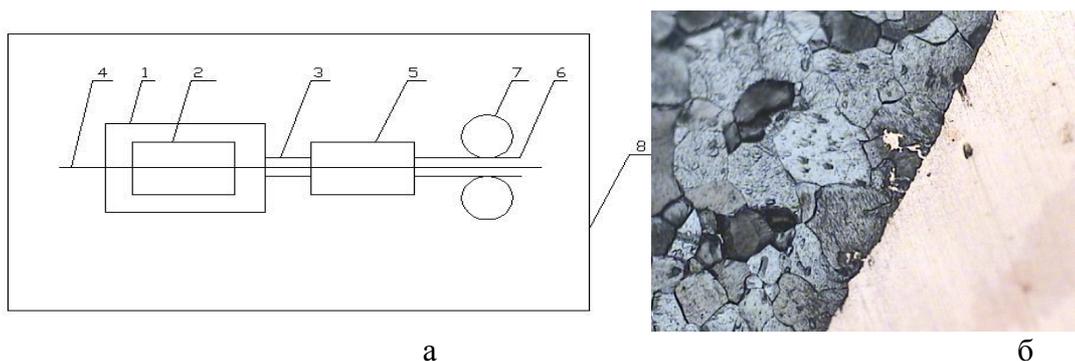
Схема технологии получения биметаллической полунепрерывнолитой заготовки (а) – обозначения в тексте и фото зоны контакта слоев сталемедной заготовки в травленном шлифе, x200 (б)
